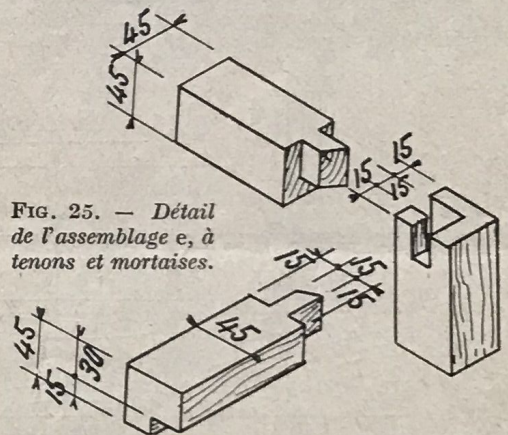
Détail de l'assemblage e, à tenons et mortaises.
